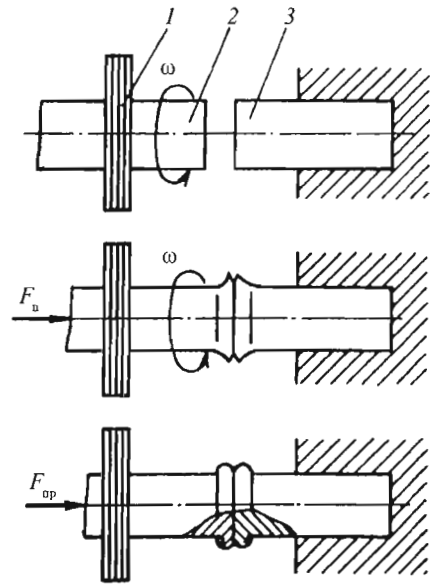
Схема инерционной сварки трением:
